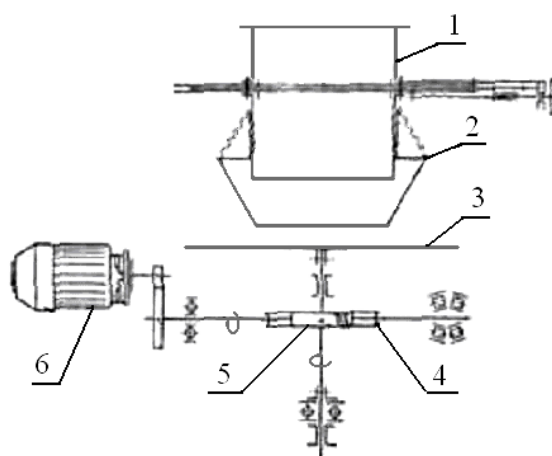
Кинематическая схема тарельчатого питателя:
